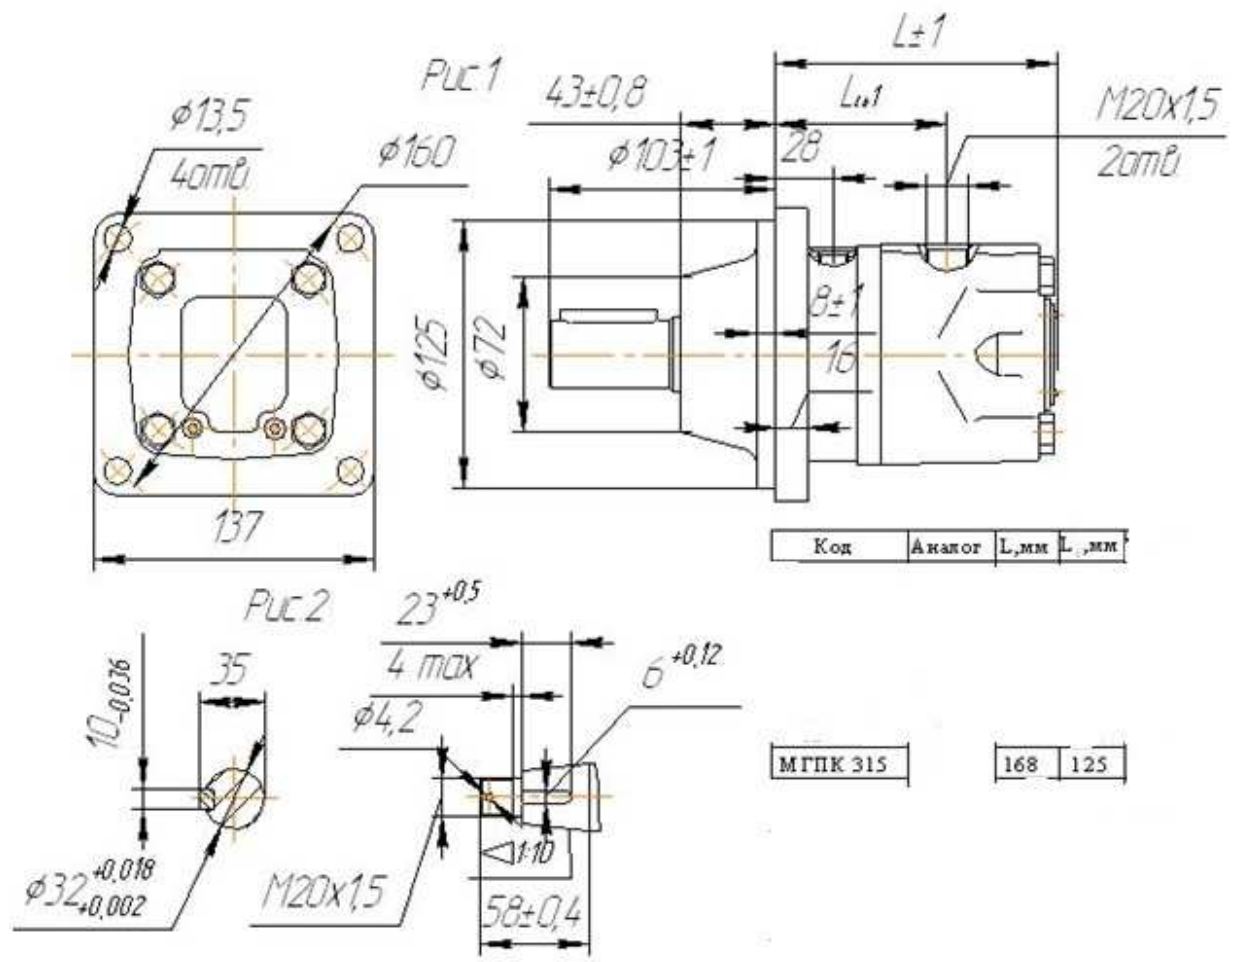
Габаритно-присоединительные размеры гидромотора типа МГПК-315
